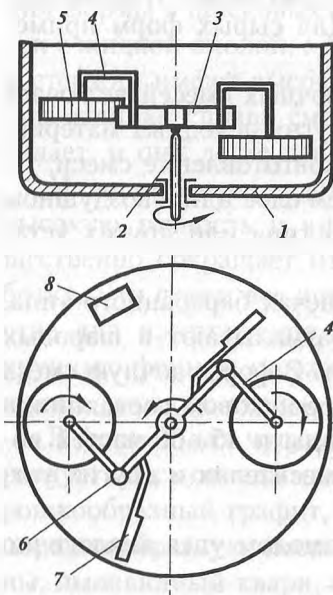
Смешивающие бегуны с горизонтальными катками: 1 — чаша; 2 — вертикальный вал; 3 — траверса; 4 — маятники; 5 — катки; 6 — шарниры; 7 — плужки; 8 — люк для удаления смеси
